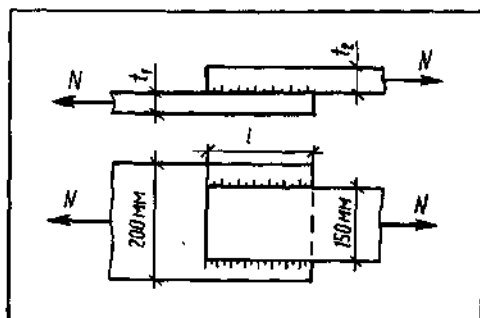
Схема сварного соединения (пример 3.2)
